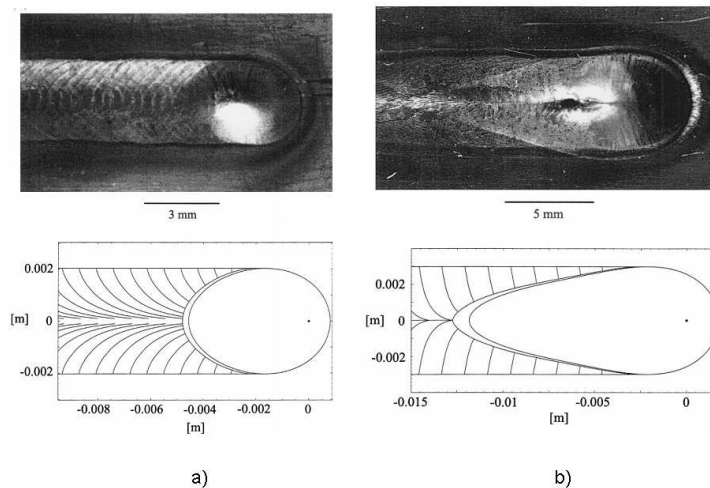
Forme du bain de fusion et morphologie des grains colonnaires, pour une vitesse de soudage faible (a) et élevée (b) [42]
